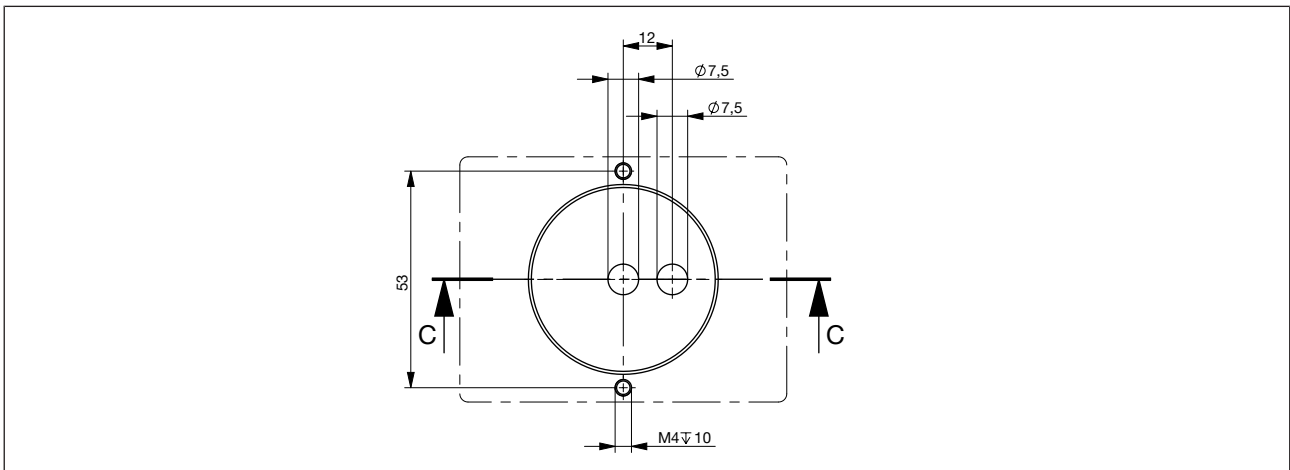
Anschlussbild 2 Einsteckflansch-Variante FC23
